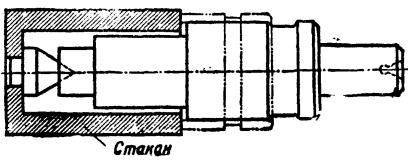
Стакан с центром для точной установки обрабатываемой детали на оправку.
